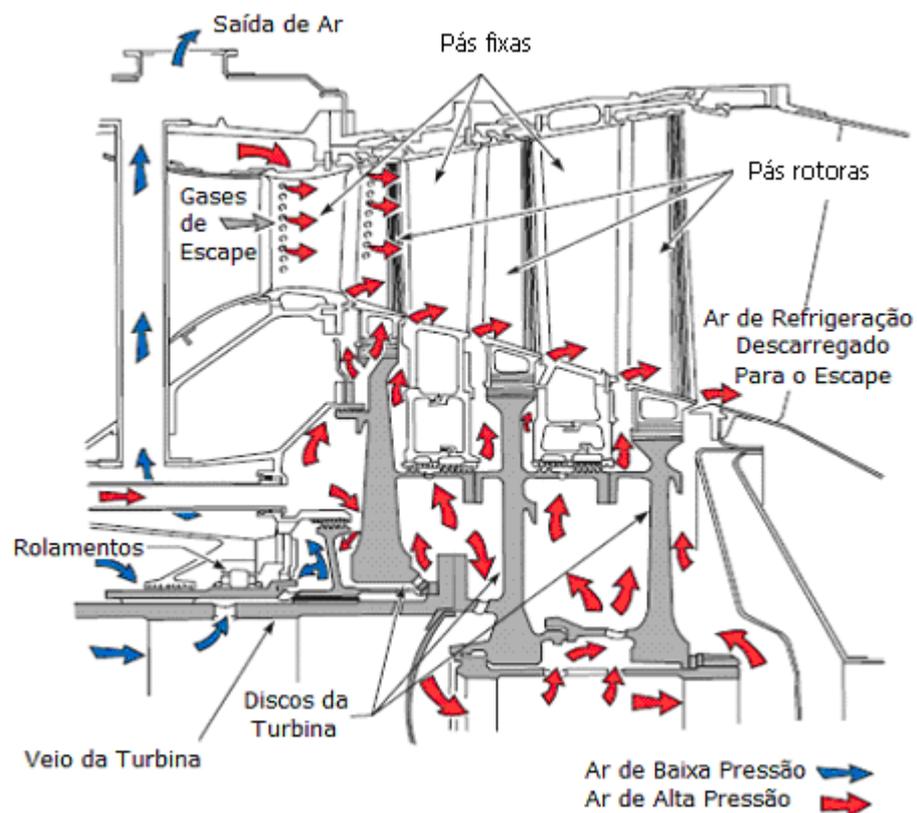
Refrigeração dos componentes internos por sangria de ar do compressor
